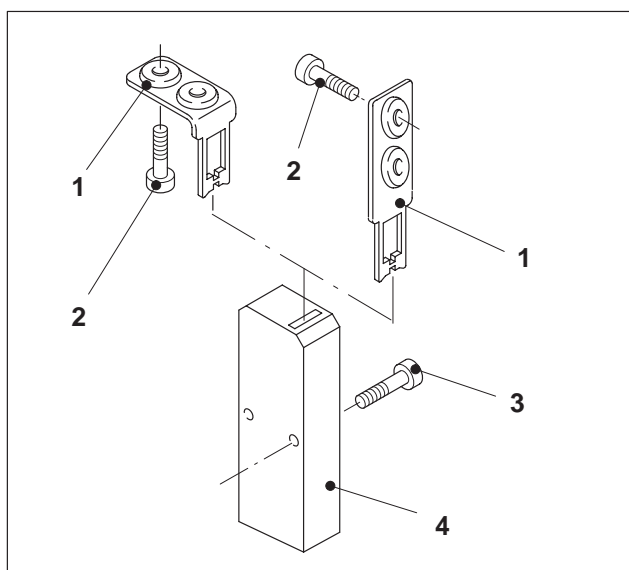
Schlüsselschalter mit gewinkeltm oder geradem Schlüssel
